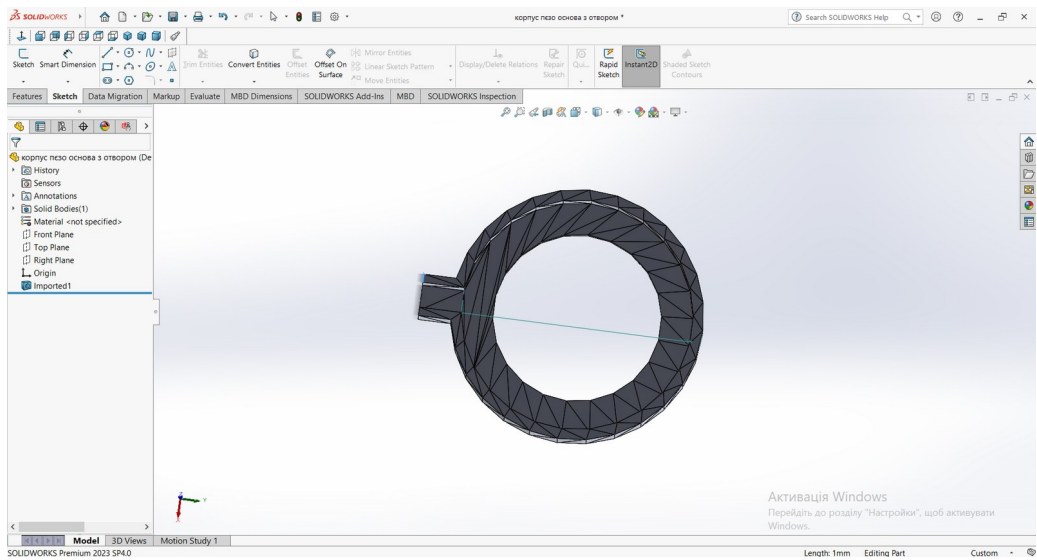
Верхній вид корпусу п’єзосенсорного модуля, спроектованого у SolidWorks
